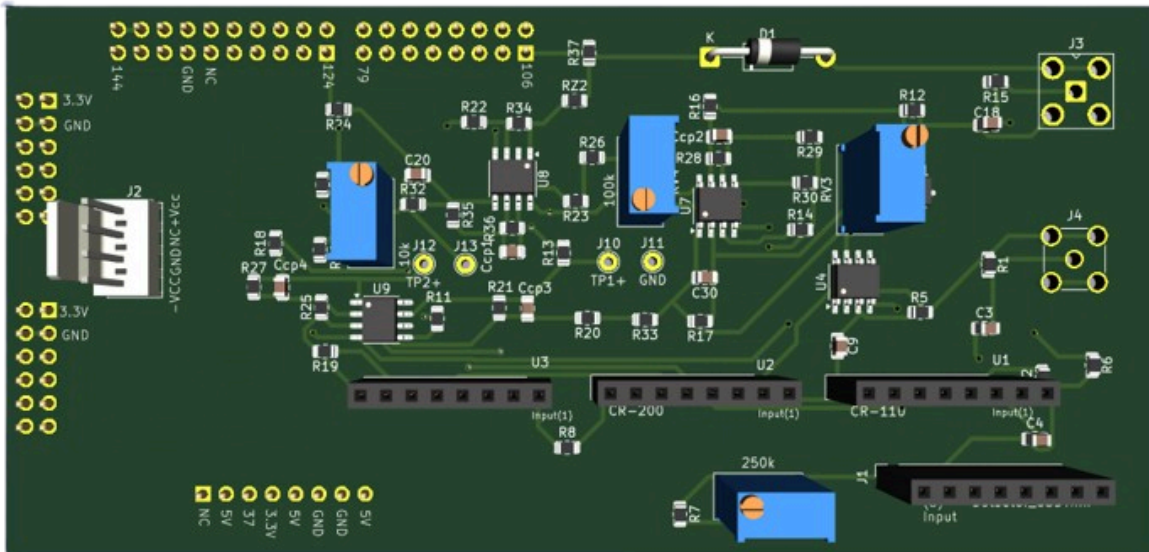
Capa superior (Top Layer). Vista 3D del diseño de PCB de KiCad,
